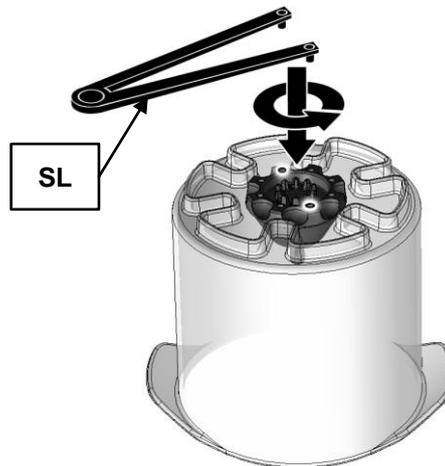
Messerdom mit Stirnlochschlüssel entfernen
